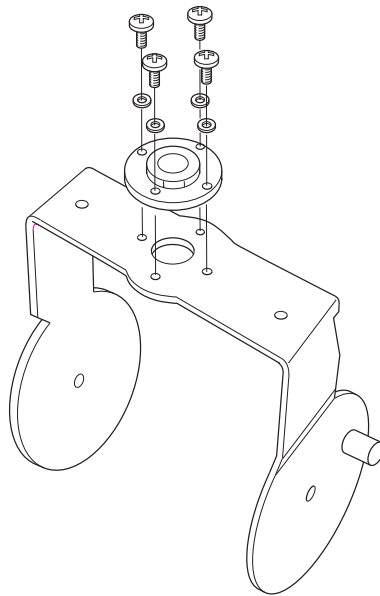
Installazione della piastra alla staffa di sospensione in caso di montaggio su una base da terra.
